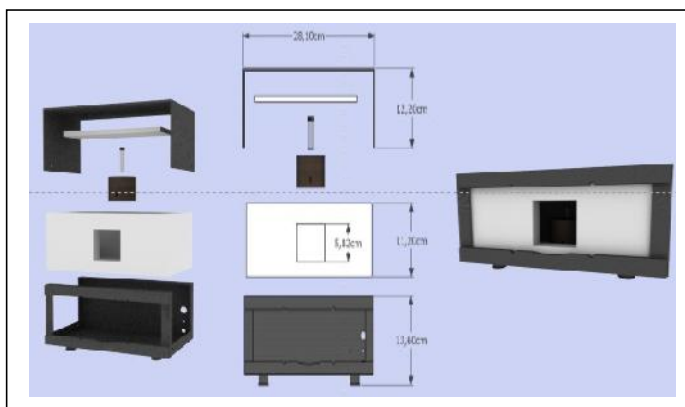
Diferentes vistas del diseño mecánico del prototipo de incubadora de laboratorio
